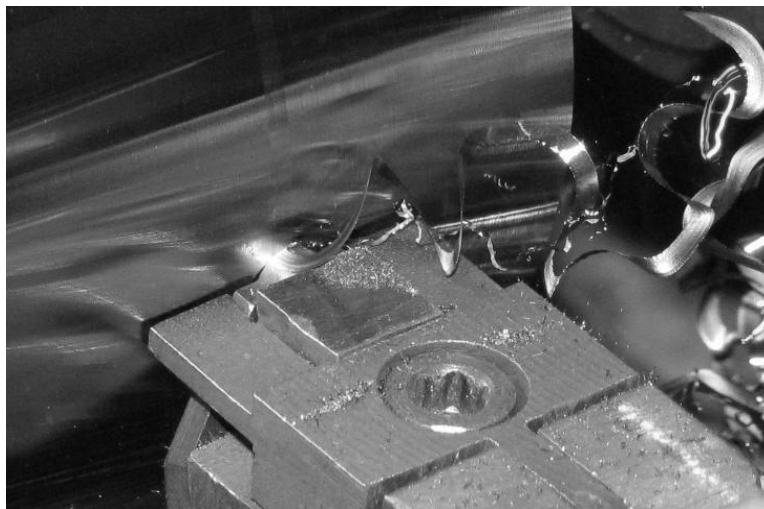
Точение резцом с цилиндрической передней поверхностью
